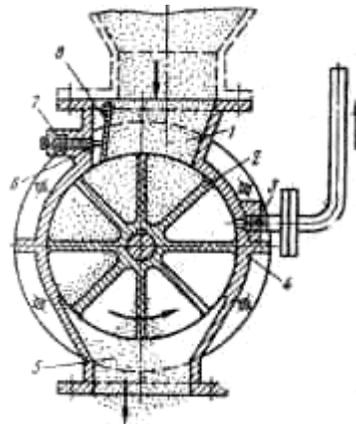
Шлюзовый затвор: 1 — приемная воронка; 2 — вращающийся лопастной барабан; 3 — труба для уравнивания давления в ячейке и приемной воронке; 4 — корпус затвора; 5 — разгрузочная воронка; 6 — штифт; 7 — пружина; 8 — скребок для предотвращения попадания твердых частиц в зазор между лопастью барабана и корпусом.
